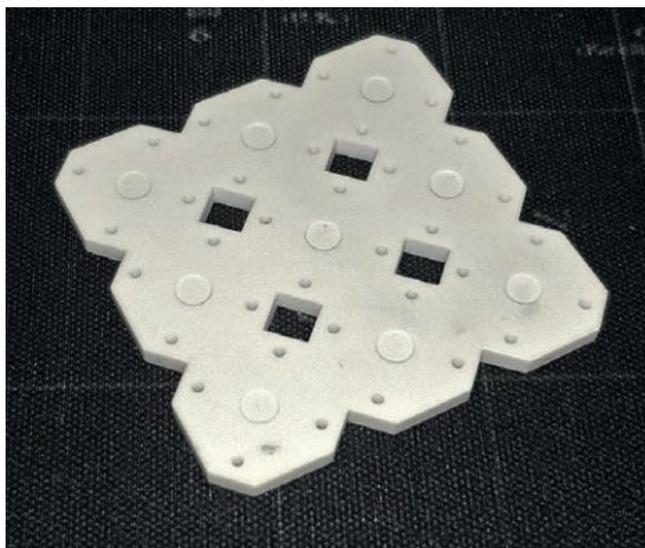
Сверление отверстий в керамике УФ - лазером [57].
